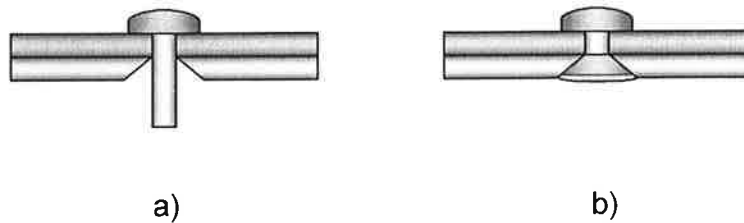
a) Placas a unir con zanco para riveteado.
